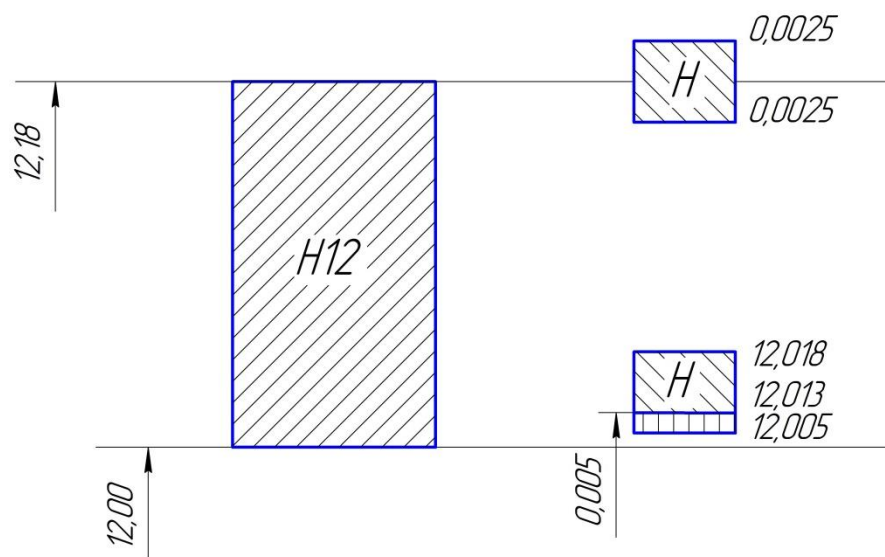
Ескіз поля допуску робочого калібру пробки для отвору $\varnothing 12H12$.
